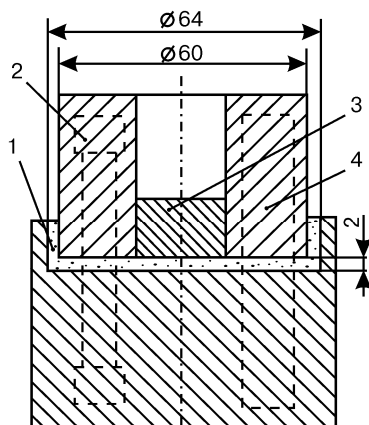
Схема паяного зразка: 1 – паяльний зазор з наповнювачем; 2, 4 – місця вирізування зразків для випробувань на розтягання й удар; 3 – припіп
